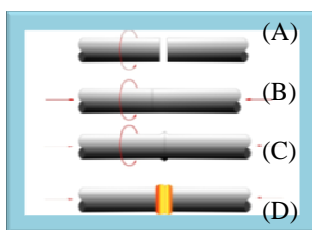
Pasos básicos de la soldadura por fricción [6].
